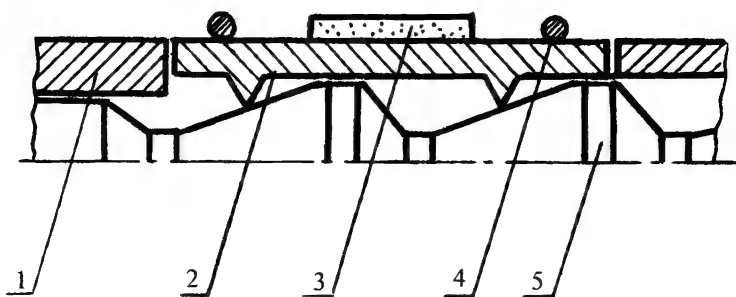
Конструктивная схема хонинговальной головки для обработки цилиндрических отверстий: 1 - корпус, 2 - колодка, 3 - абразивный брусок, 4 - пружинное кольцо, 5 - конусный валик
